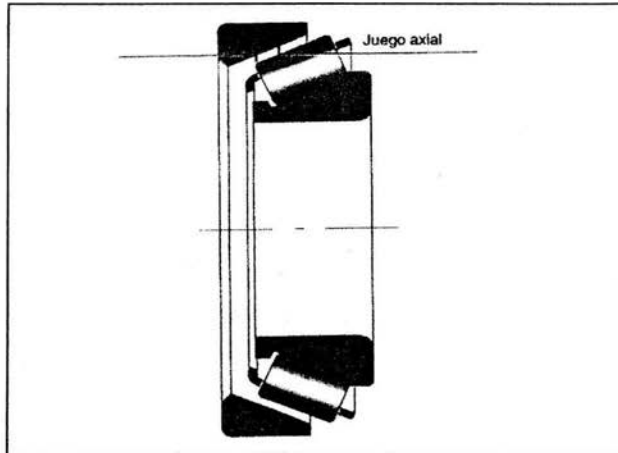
Juego interno en un rodamiento de rodillos cónicos
